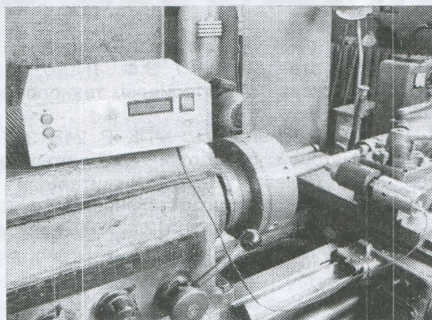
Внешний вид оборудования ультразвуковой упрочняюще-чистовой обработки поверхности вала с технологическими отверстиями на базе токарно-винторезного станка мод. 1К62
